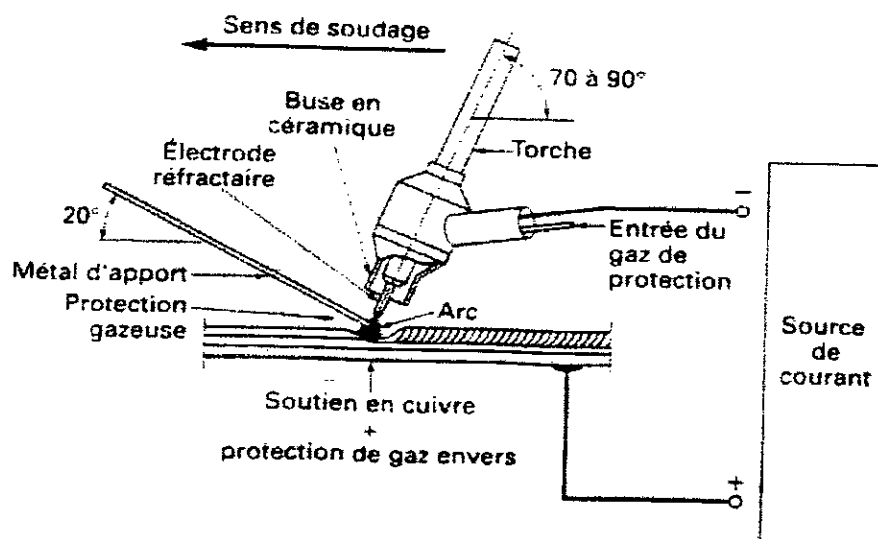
Principe du soudage (manuel) à l'arc électrique avec électrode réfractaire (GTAW) [24].
